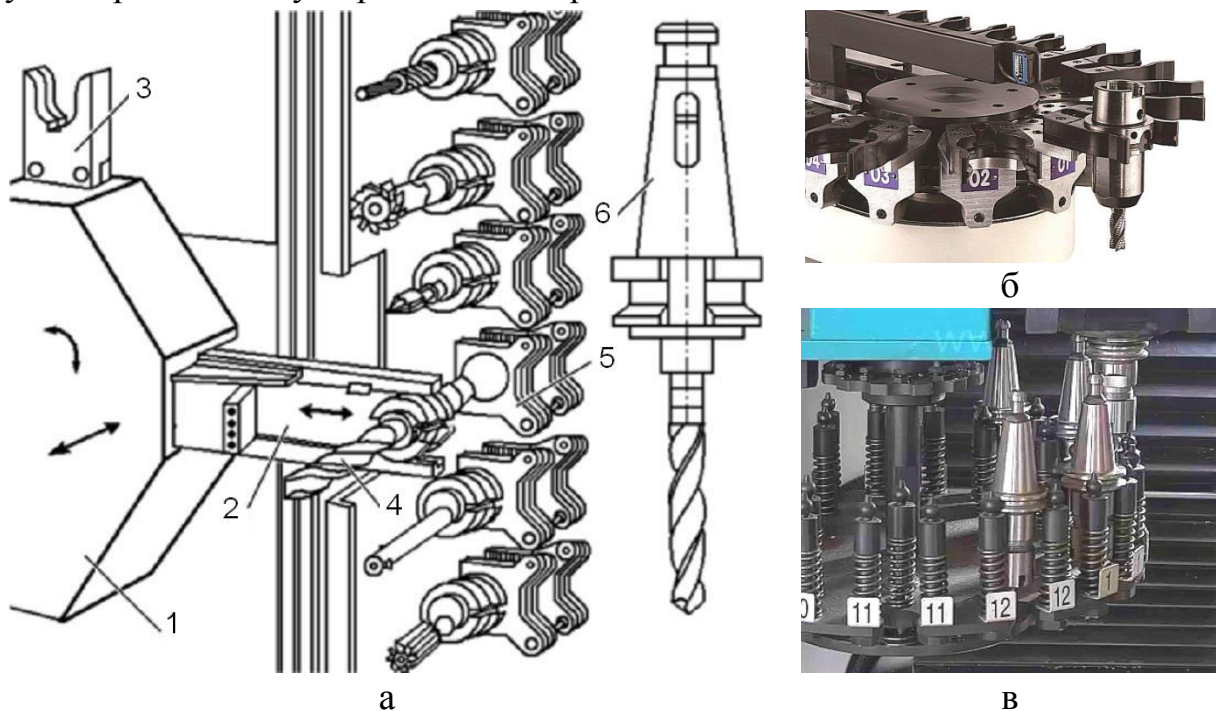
Схема пристрою АЗІ (а), зовнішній вигляд механізму захоплення (б) та інструментальної обойми (в): 1 – корпус захоплювача; 2 – важіль захоплювача; 3 – захоплювач; 4 – інструмент; 5 – гніздо ланцюга інструментальної обойми; 6 – оправка конусна
